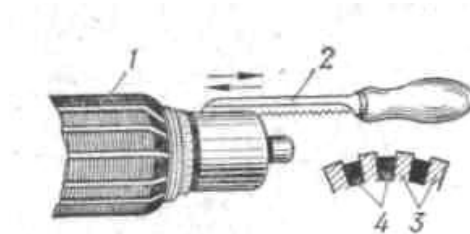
Прорізування міканіту між пластинами колектора якоря: 1 - якор; 2 - ножівка; 3 - колекторні пластини; 4 - міканіт.
